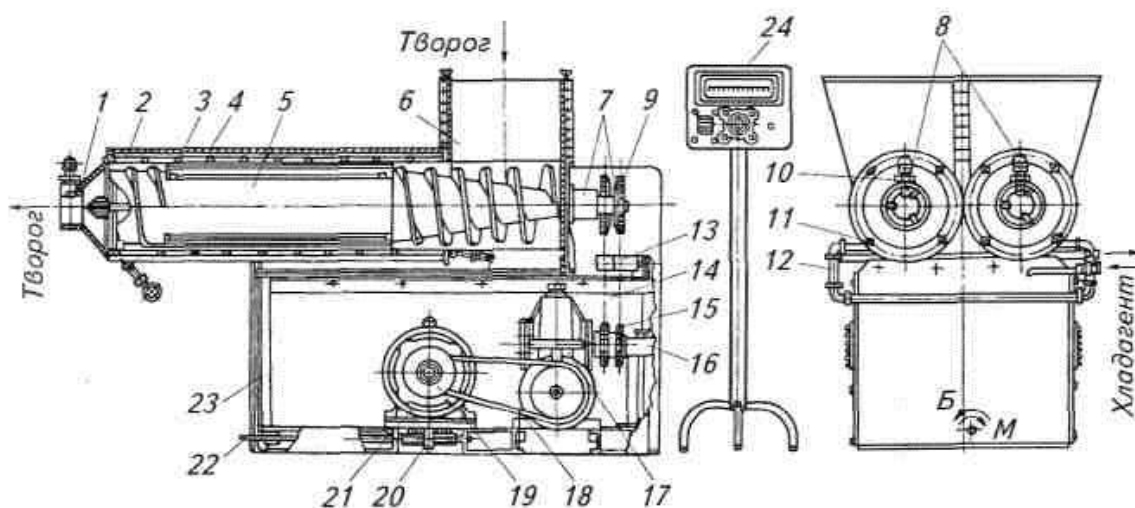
Двухцилиндровый охладитель: 1 — крышка; 2 — внутренний цилиндр; 3 — рубашка; 4 — кожух; 5 — вытеснительный барабан; 6 — полубункер; 7 — привод; 8 — цилиндры; 9 — звездочка; 10 — термометр сопротивления; 11 — зажим; 12 — коллектор для хладоносителя; 13 — натяжное устройство; 14 — цепь; 15 — звездочка редуктора; 16 — опора; 17 — редуктор; 18 — клиноременная передача; 19 — вариатор; 20 — механизм перемещения двигателя; 21 — электродвигатель; 22 — регулировочный винт; 23 — станина; 24 — пульт управления
